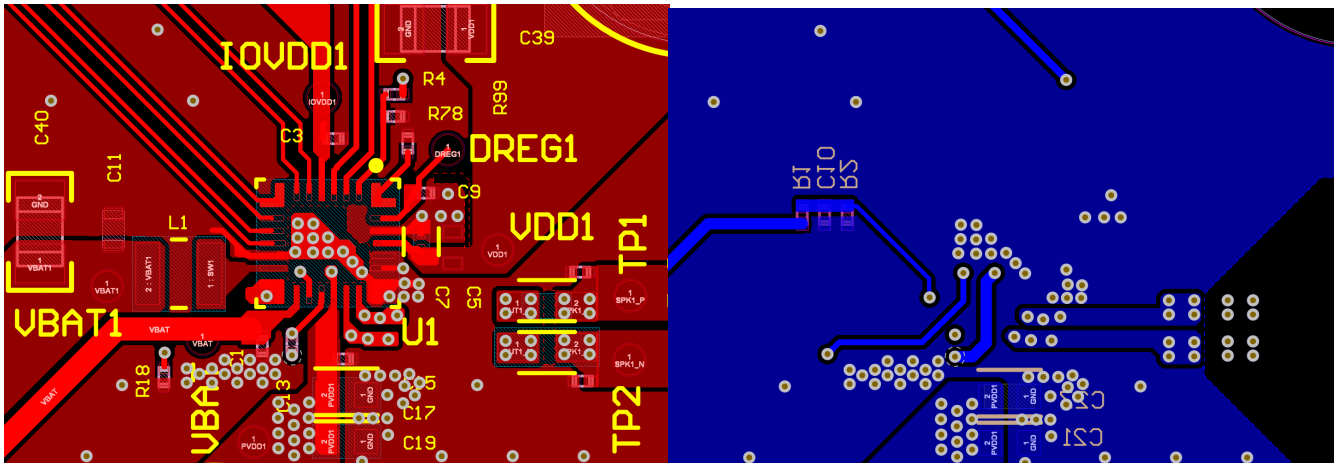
顶层 (红色) 和底层 (蓝色) — 软件控制参考 PCB 布局
